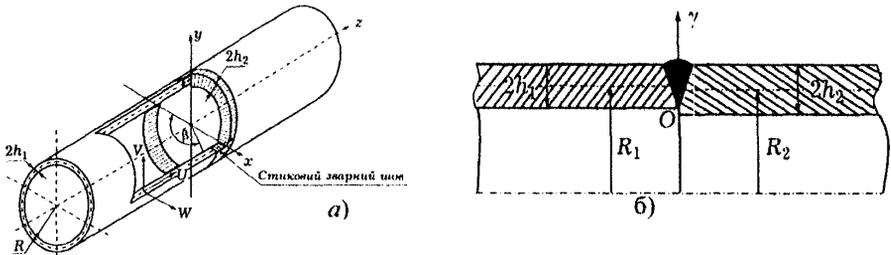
Схема стикового зварного з'єднання різновтовщинних труб у вигляді замкнених колових циліндричних оболонок (а), осьовий переріз зварного з'єднання (б)
